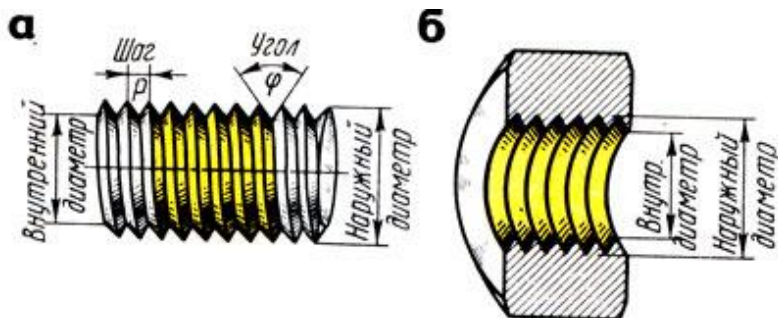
Детали с резьбой: а - наружной (болт), б - внутренней (гайка)
